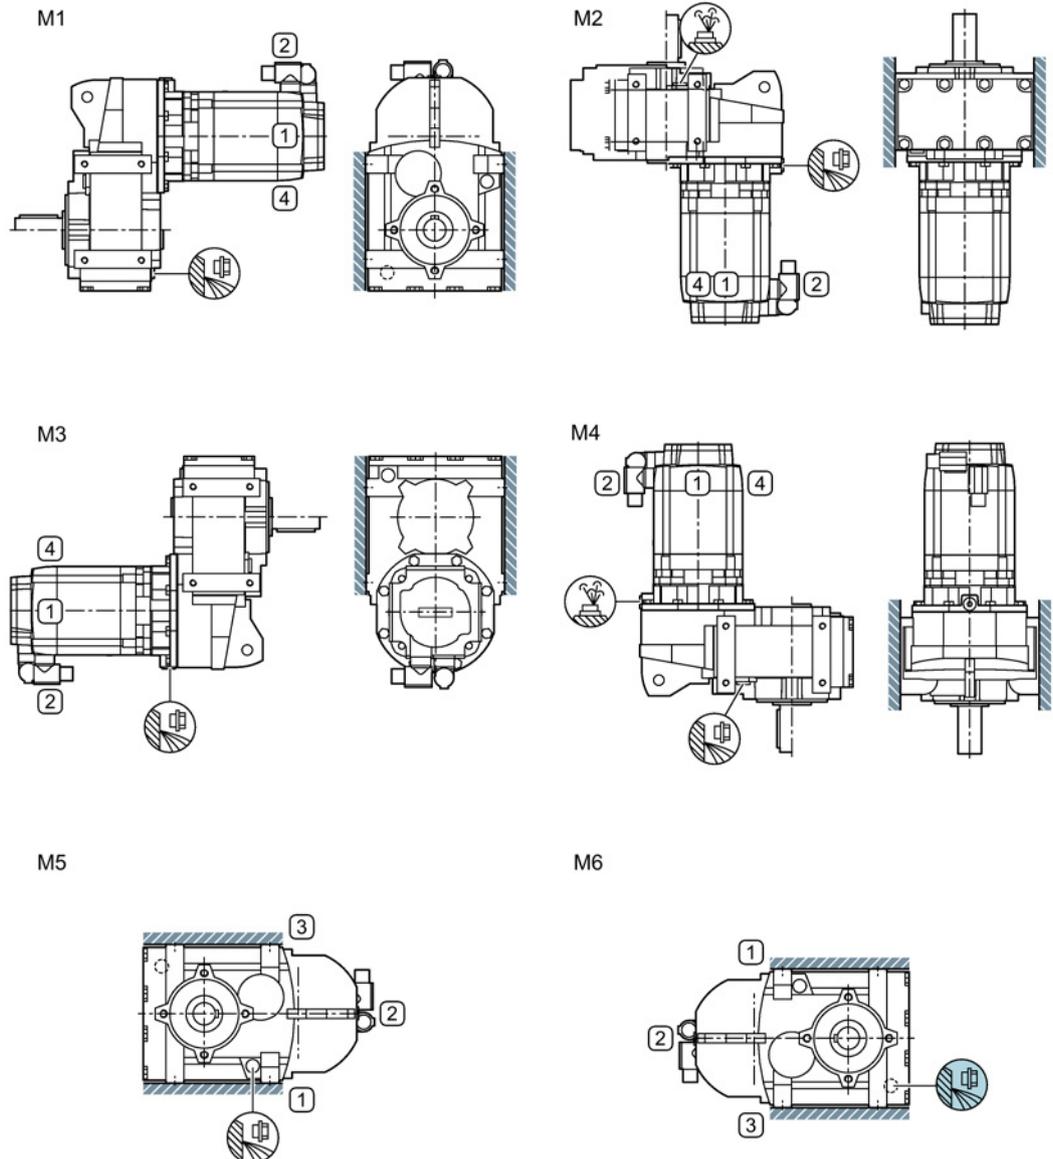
Einbautagen für Flachgetriebe FZ und FD, Fußausführung, Baugröße 29, 2-stufig und 3-stufig
